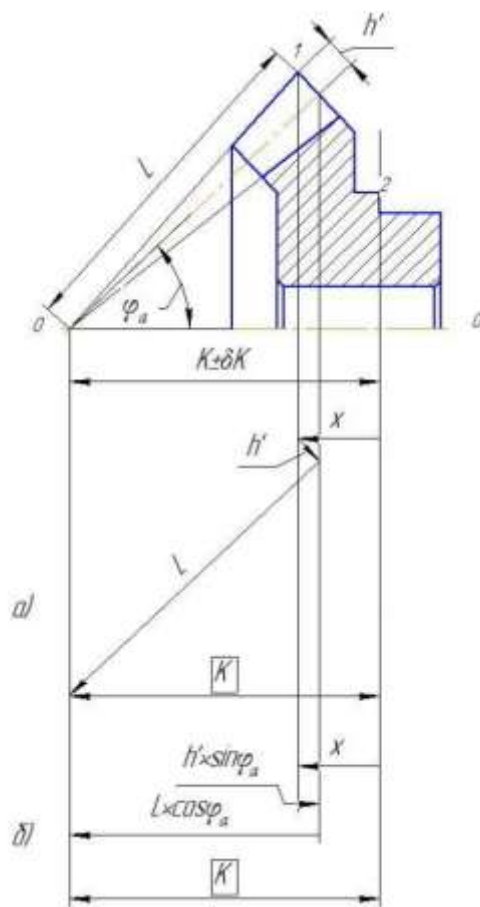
Креслення конічної шестерні і схеми розмірного ланцюга.
